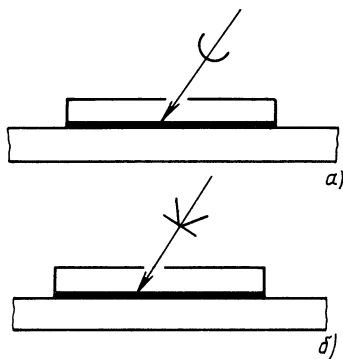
Условные знаки для обозначения паяного (а) и клееного (б) соединений
